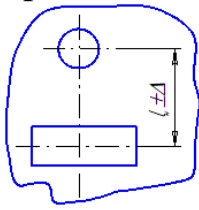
Схема размеров и полей допусков штампуемой детали и рабочих деталей штампа при их совместном изготовлении:
